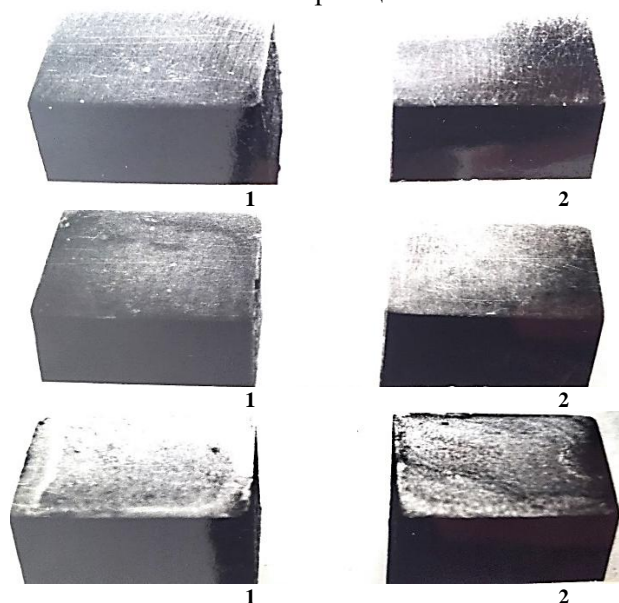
Фотография образцов, изготовленных из обрабатываемого материала сталь 45.
